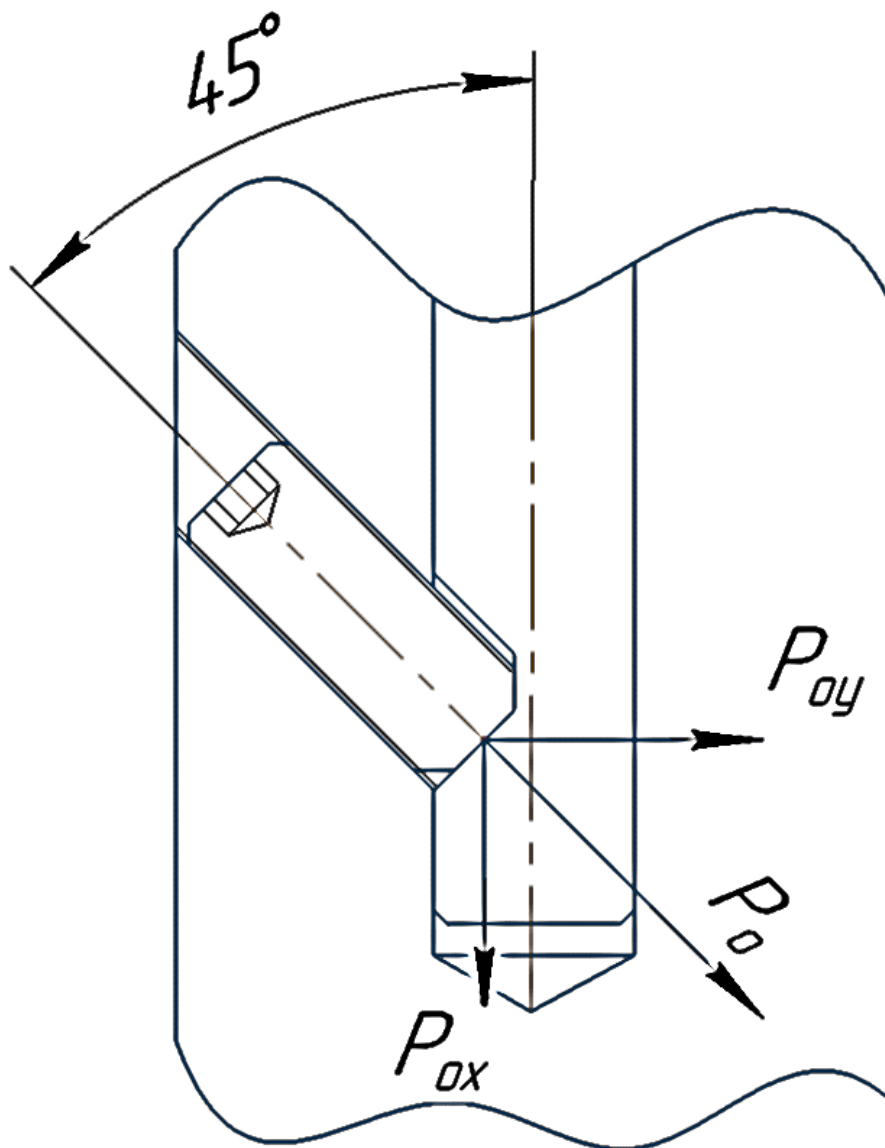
Схема закріплення змінної головки в корпусі свердла
